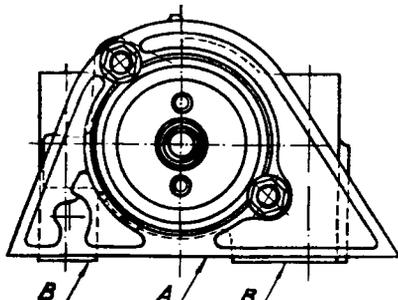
Установка держателя сальника распределительного вала: А - нижняя плоскость держателя; В - нижняя плоскость корпуса подшипников распределительного вала
